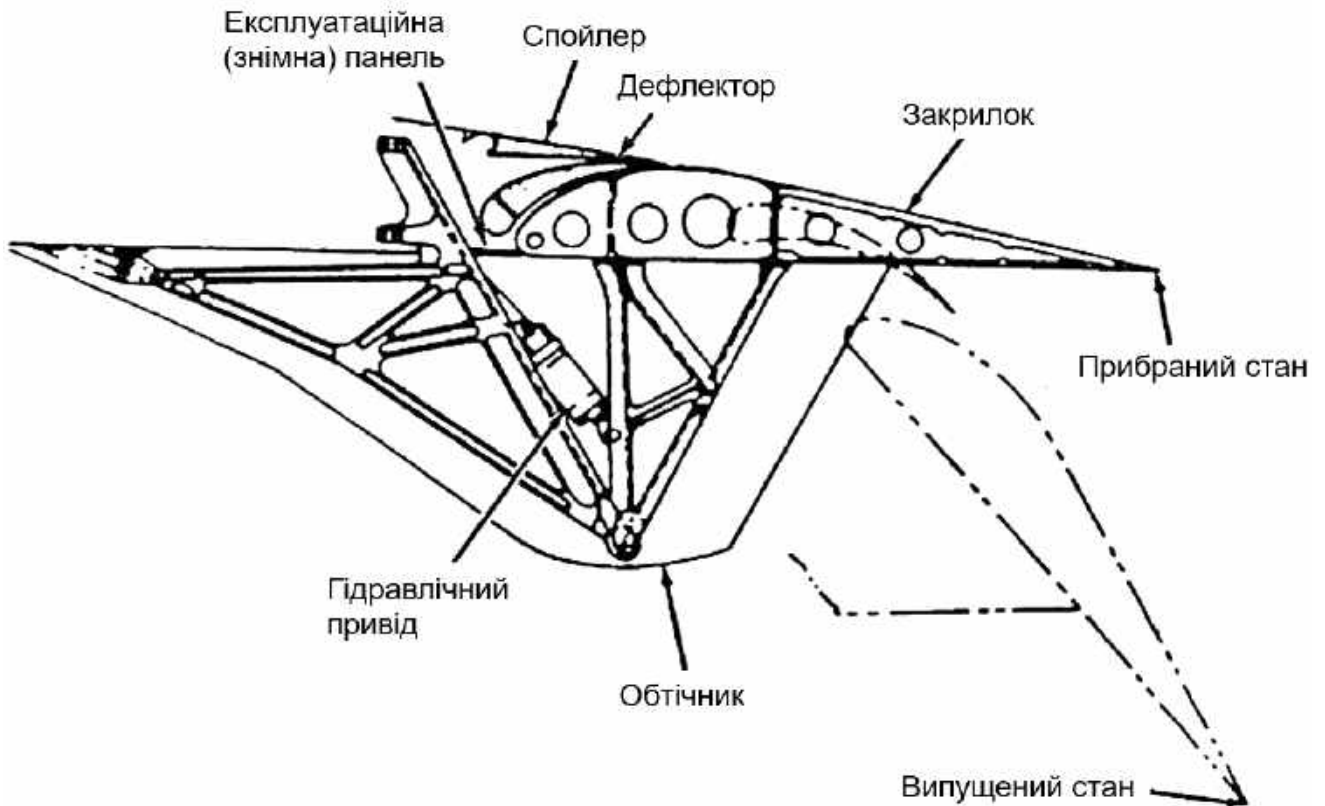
Схема поворотного двощільного закрилка літака DC-10 [93]
